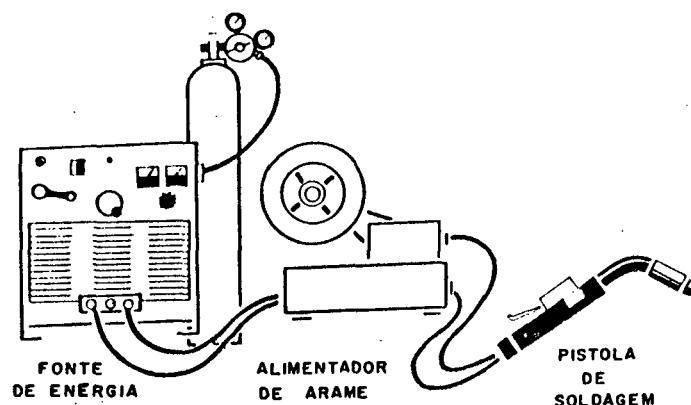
Equipamento para soldagem MIG/MAG [1].
